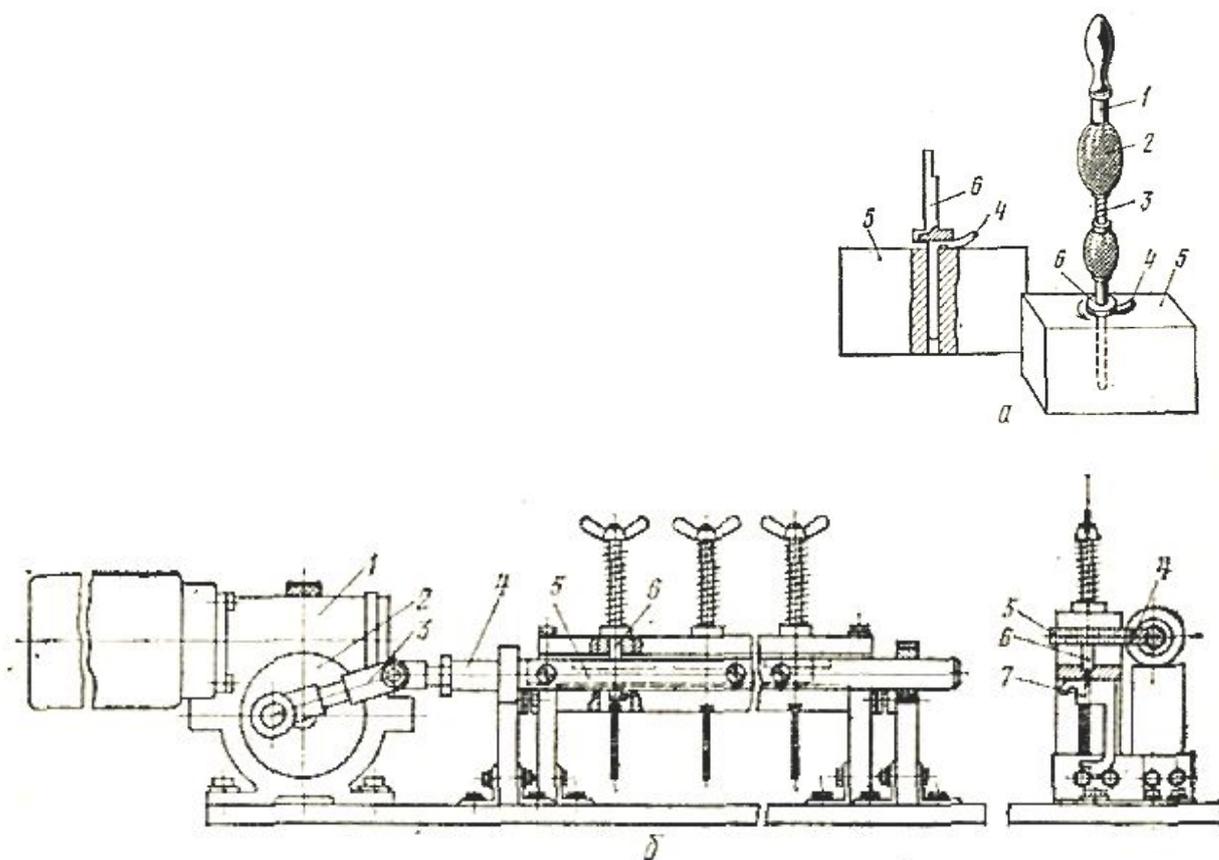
Приспособления для притирки лапок нитеуловителей.
